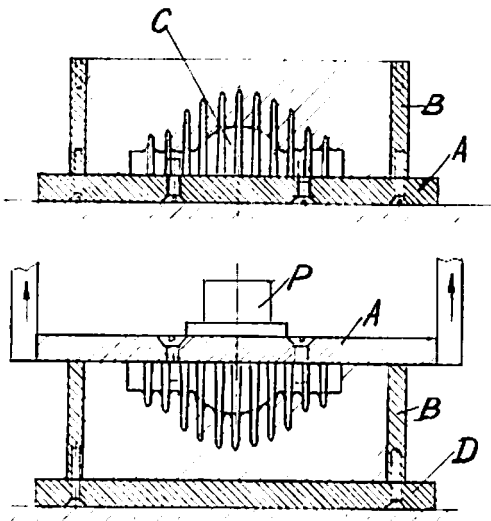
Zylinderkopfhälfte auf der Formmaschine.
